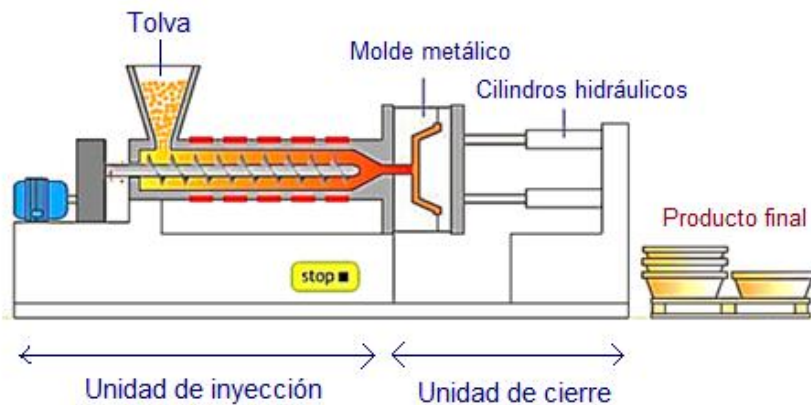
Sección transversal de una máquina de molde por inyección.
